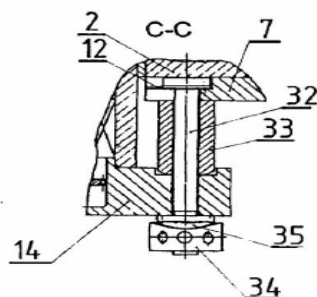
Механізми осьової фіксації нижнього валка розріз [8]
